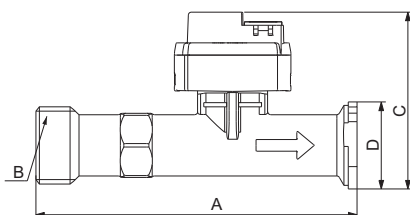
Размеры, VFS QT, 1-15 л/мин, овальный фланец
